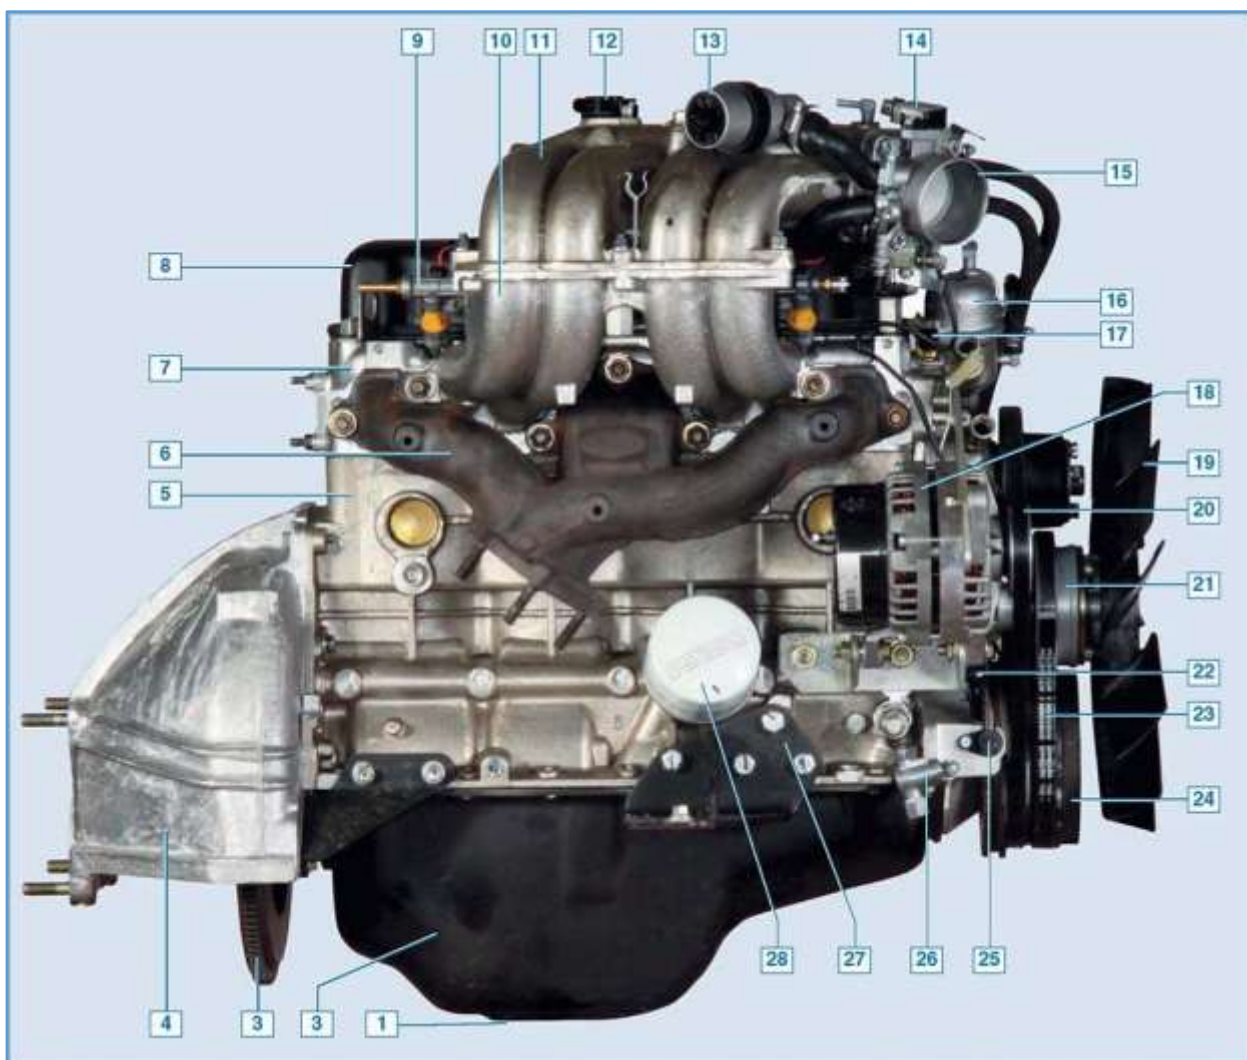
Двигатель (вид слева по направлению движения автомобиля)
